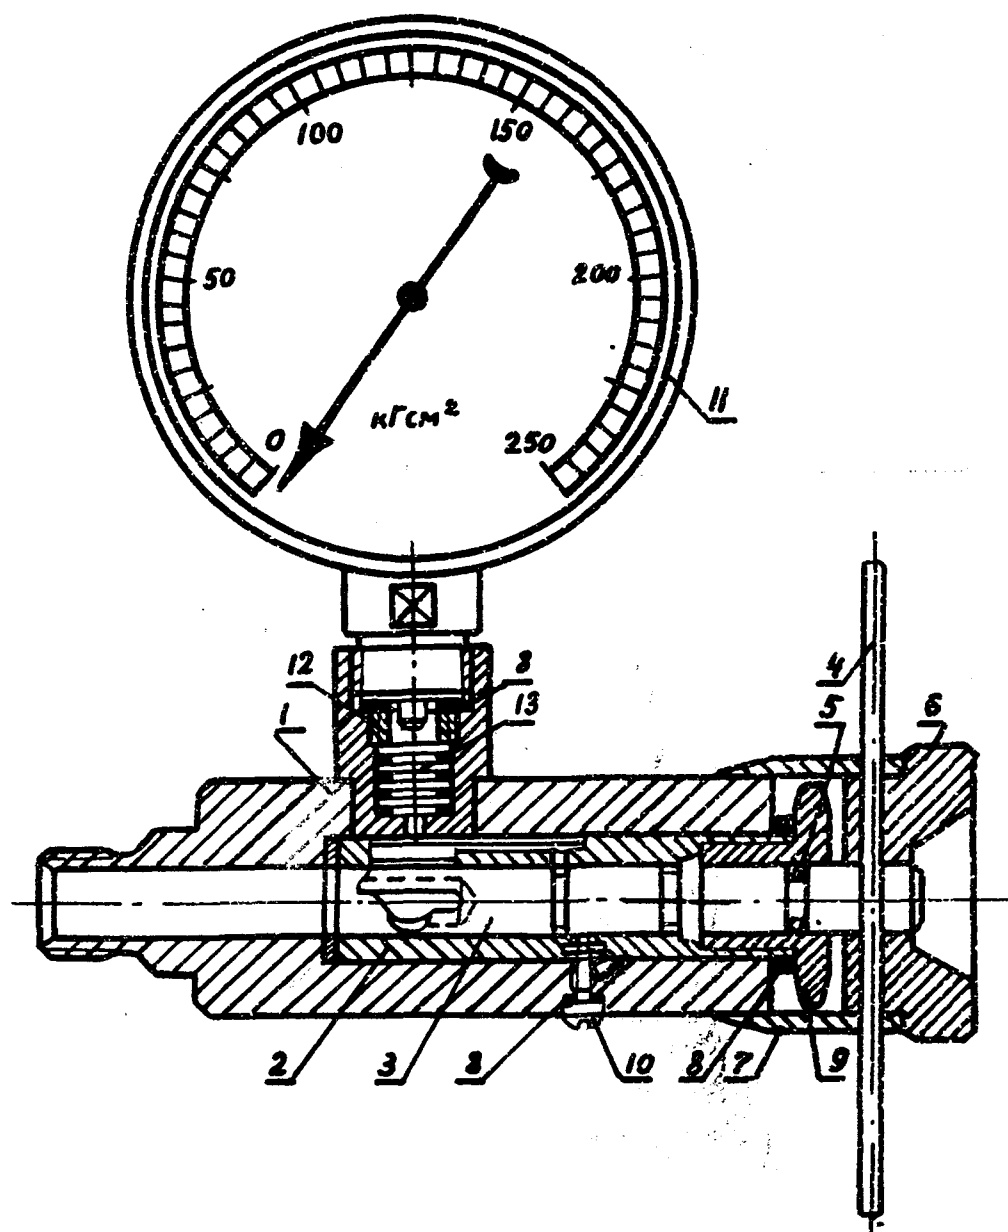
Прибор КИ-1097: 1 - корпус; 2 - гильза; 3 - плунжер; 4 - стержень; 5 - уплотнительное кольцо; 6 - рукоятка прибора; 7 - конус; 8 - уплотнительная прокладка; 9 - упорная гайка; 10 - установочный винт; 11 - манометр; 12 - гайка; 13 - демпфер
